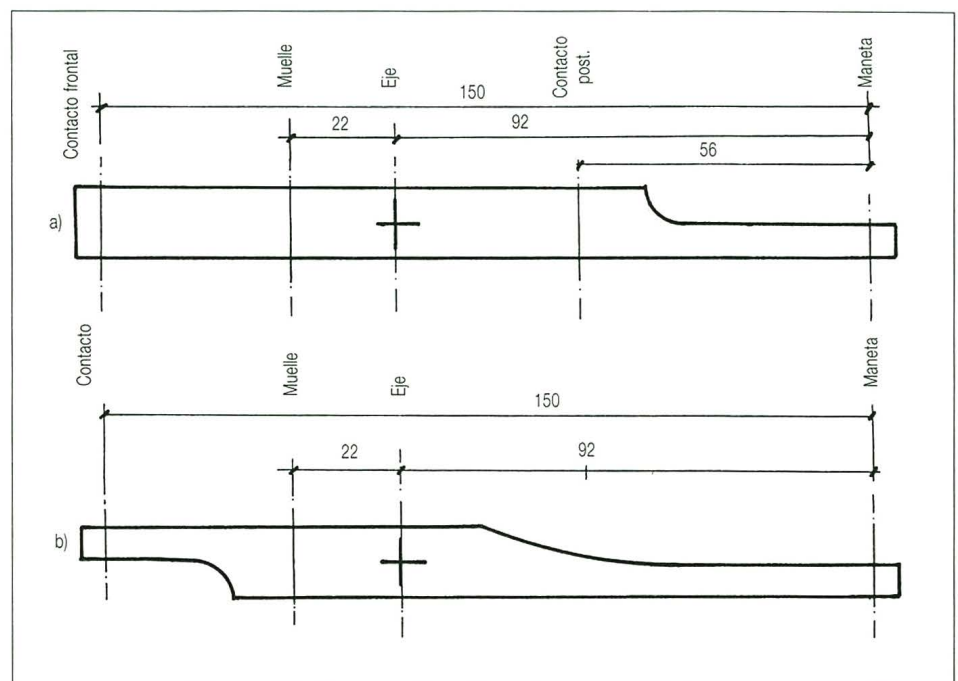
Brazo de manipulador. a) Clásico. b) Calliper.
